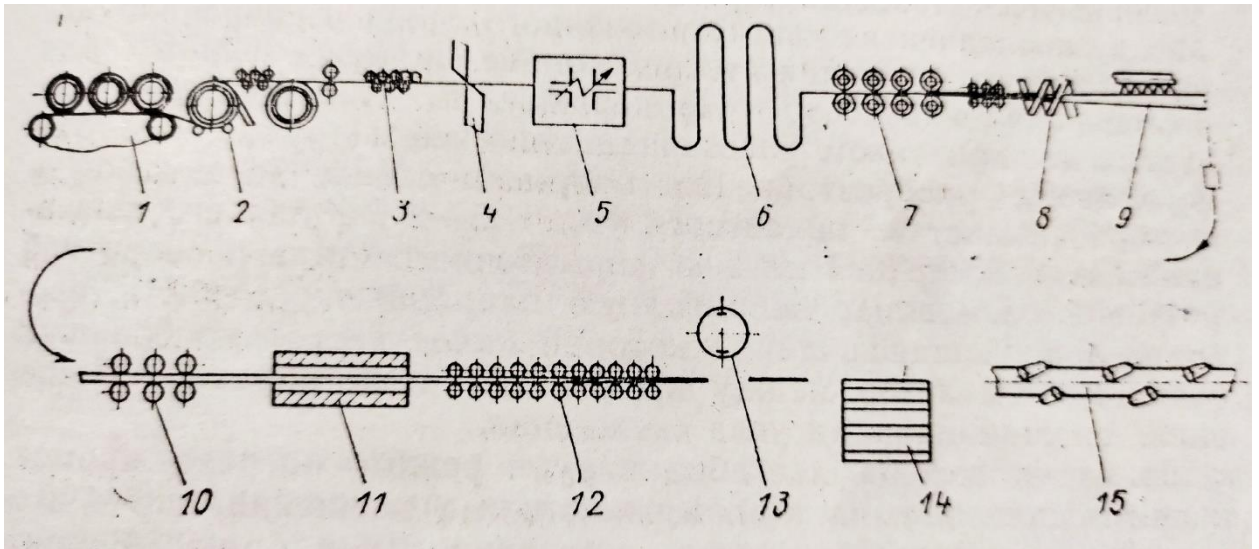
Принципиальная схема агрегата для высокочастотной сварки прямошовных труб [27]
